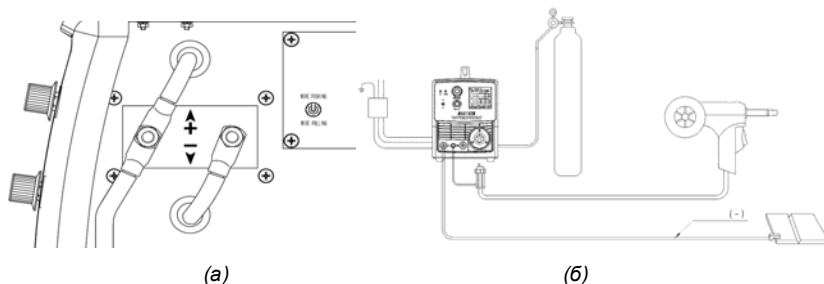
Полуавтоматическая сварка алюминия алюминиевой проволокой
